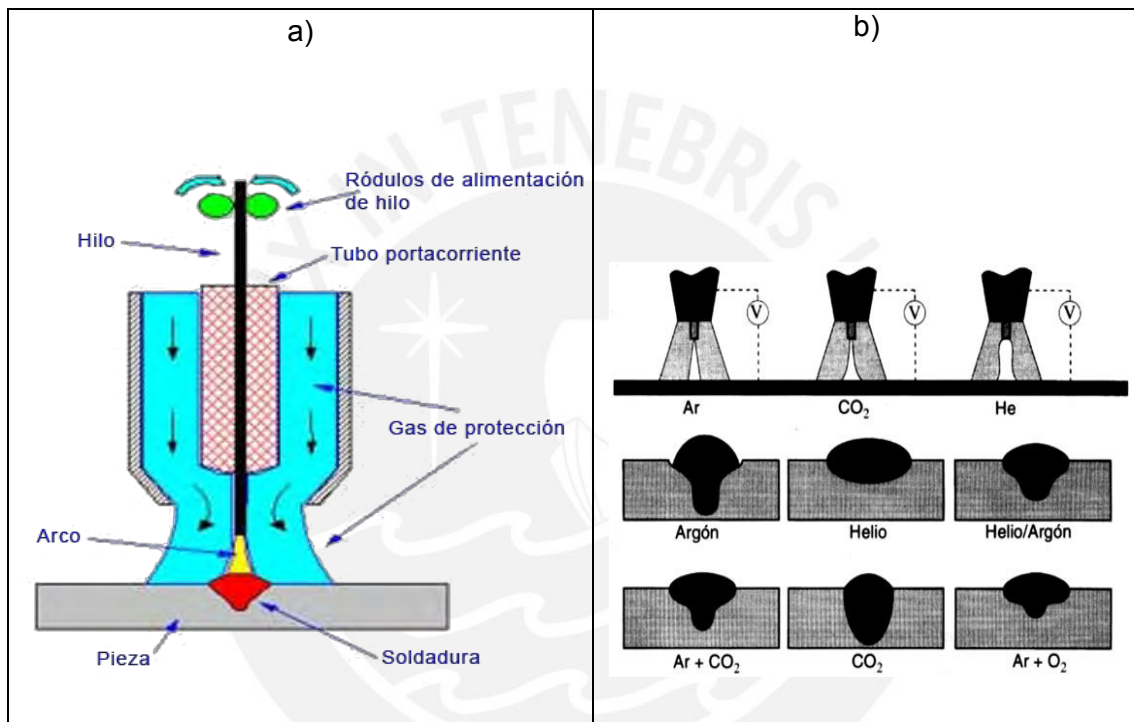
a) Esquema de proceso de soldadura GMAW, b) forma de cordón debido a la composición de gas protector; Fuente: brusiterrades.com y Manual del Soldador, CESOL respectivamente
